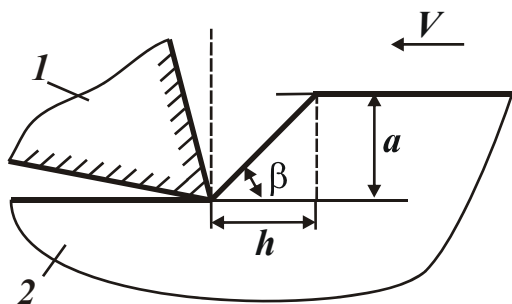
Расчетная схема процесса резания: 1 – резец; 2 – обрабатываемый материал.
